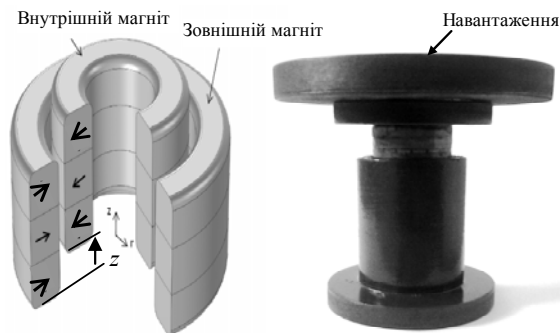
Конструкція пружини з двома циліндричними постійними магнітами
